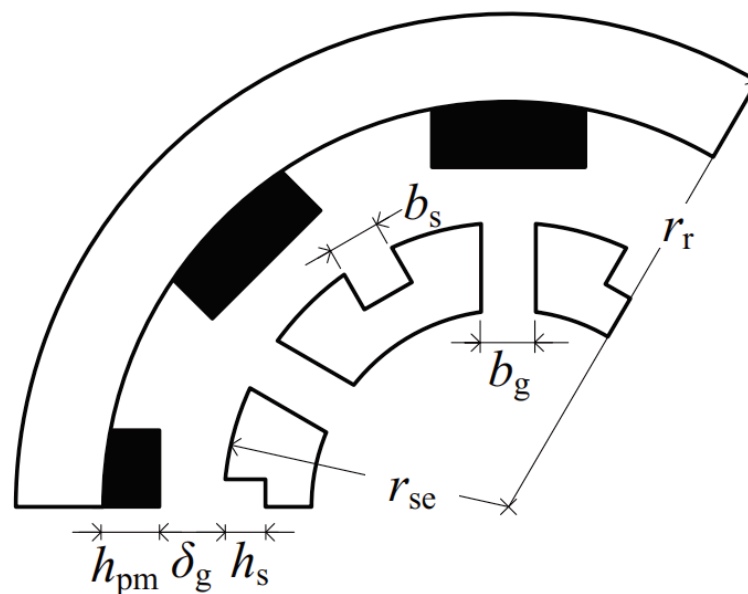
Dimensiones geométricas principales máquina 28 polos 24 ranuras.
